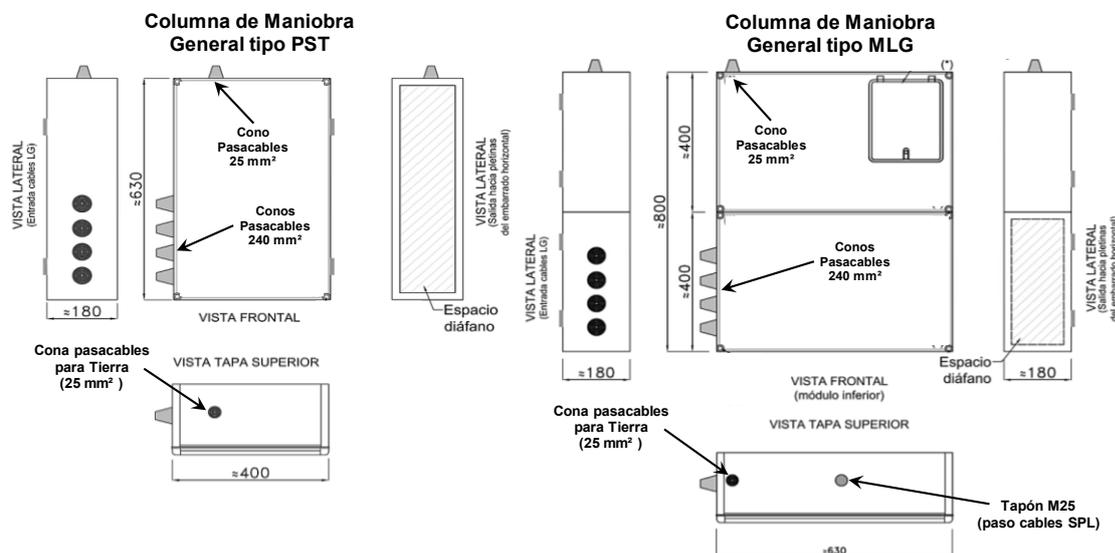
Pasacables y Tapones en Columnas de Maniobra General
